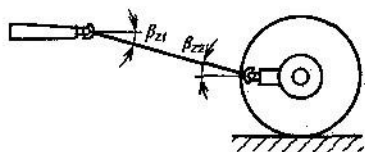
Расположение карданного вала по схеме Z (вид сбоку). Для предотвращения различных скоростей вращения на выходе коробки передач и на входе главной передачи углы β на обоих концах должны быть одинаковы (как показано на рисунке), а вилки шарниров — лежать в одной плоскости
